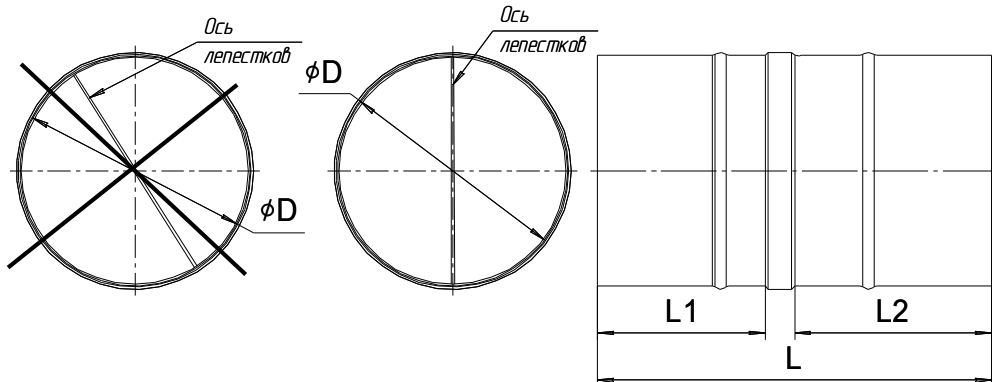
Габаритные и присоединительные размеры клапана RSK
